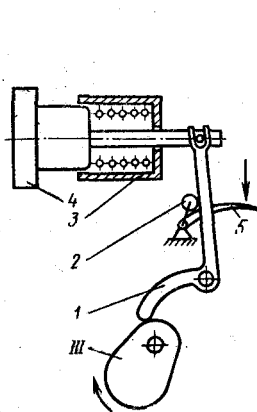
Схема механизма перемещения поддерживающего шпинделя
